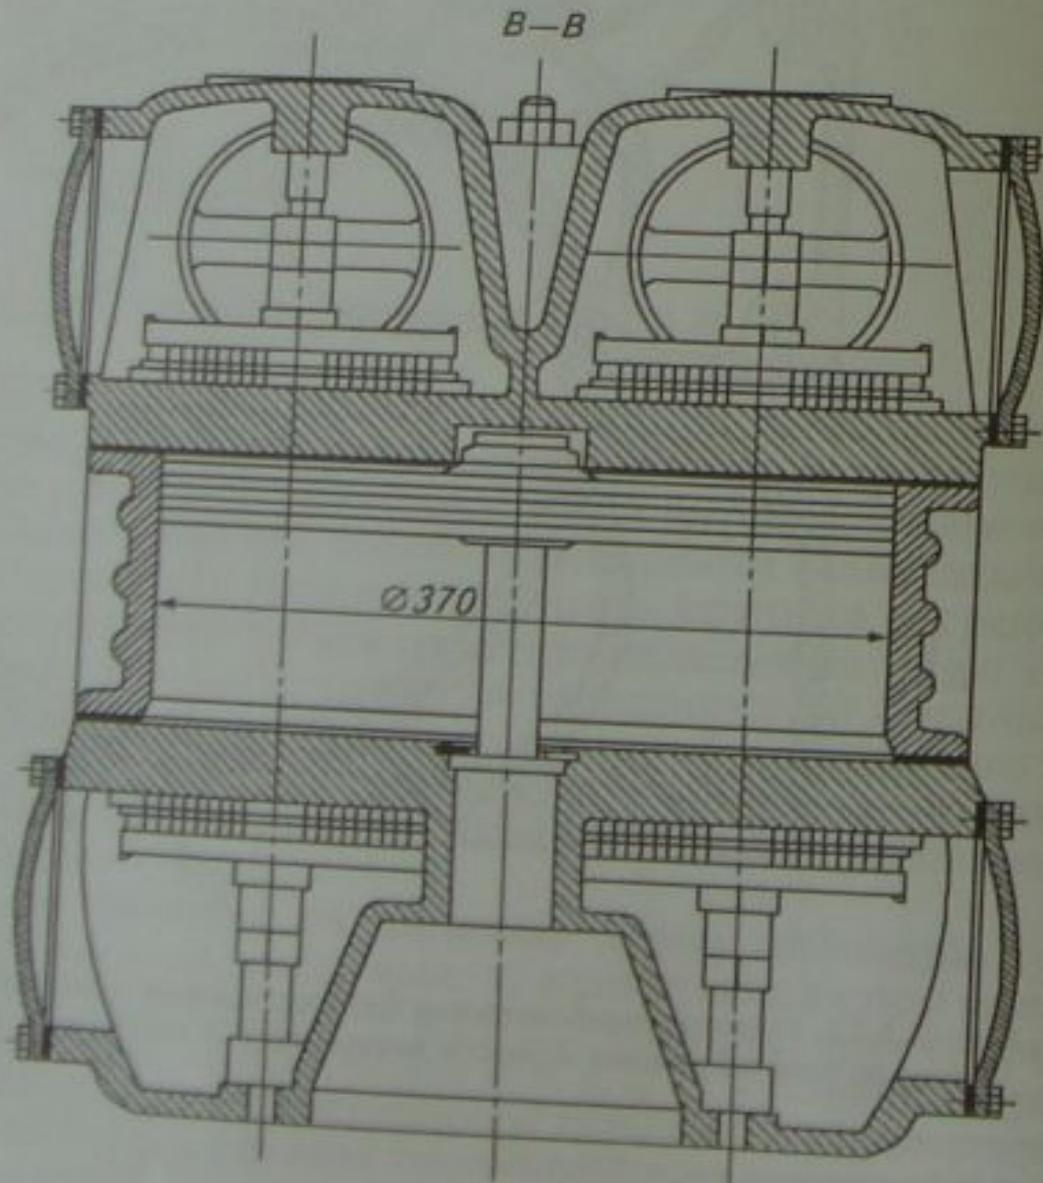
Цилиндр газового компрессора без смазки полостей сжатия:
